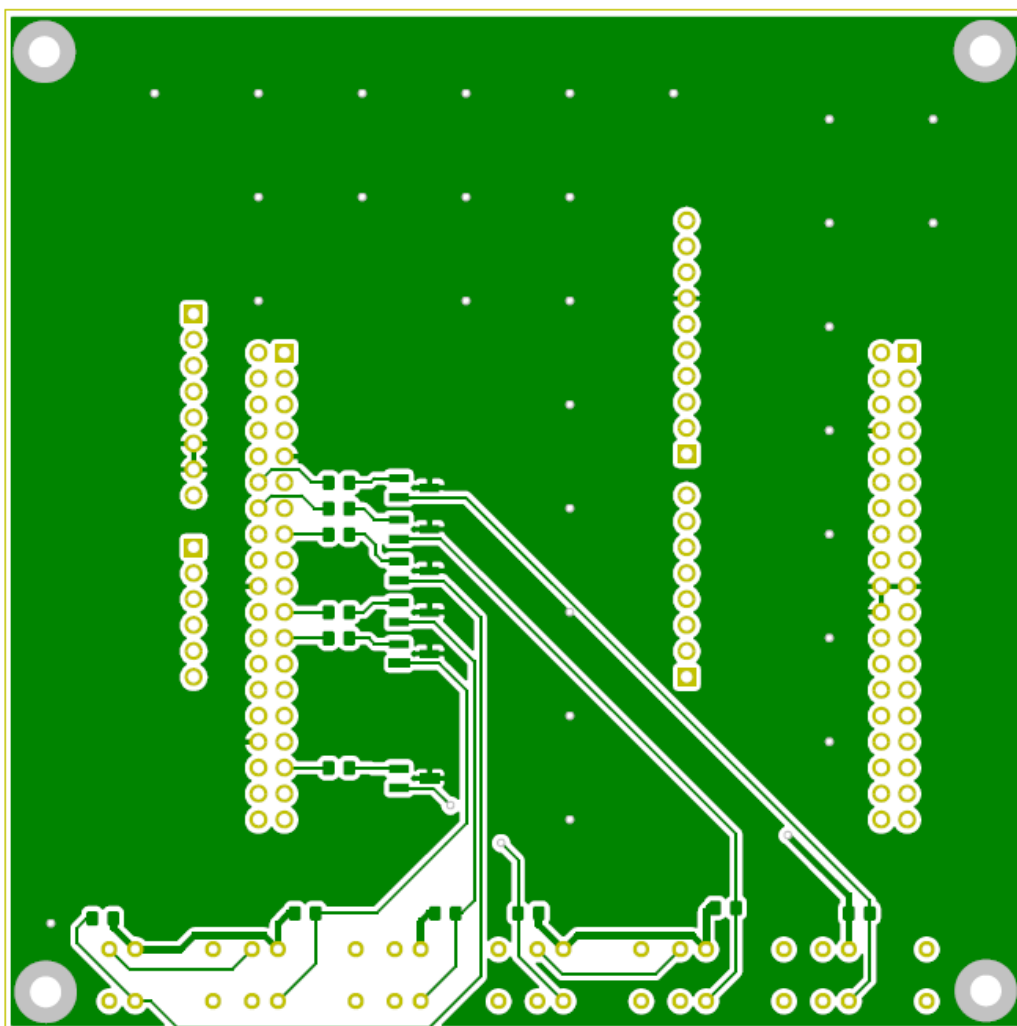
Schemat layoutu PCB łóżka testowego dla wariantu 1.
